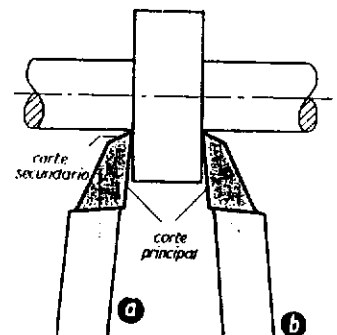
Útiles de corte lateral: a) útil de corte lateral a la izquierda; b) útil de corte lateral a la derecha.
